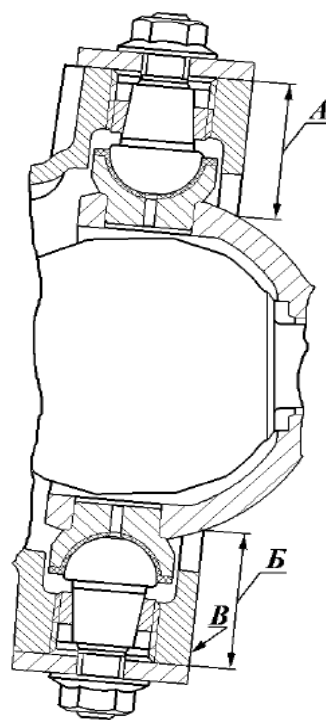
Регулировка затяжки шаровых шкворней поворотного кулака
